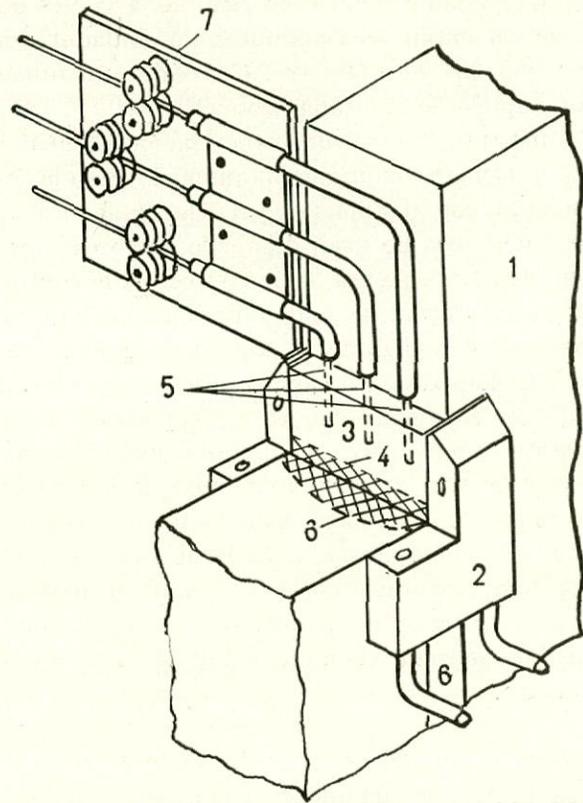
Esquema del proceso de soldadura eléctrica "Electro-slag".
